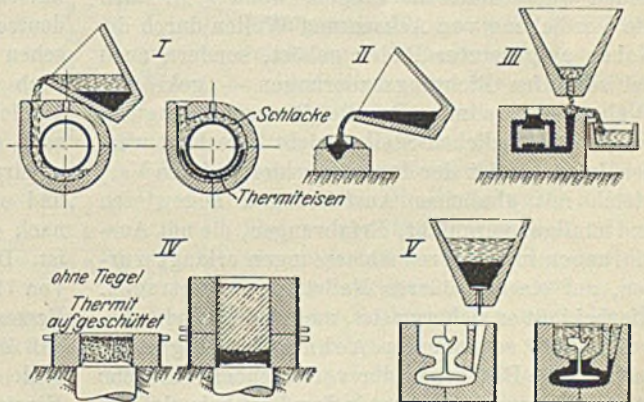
Ausführungsarten der Thermiterschweißung.
